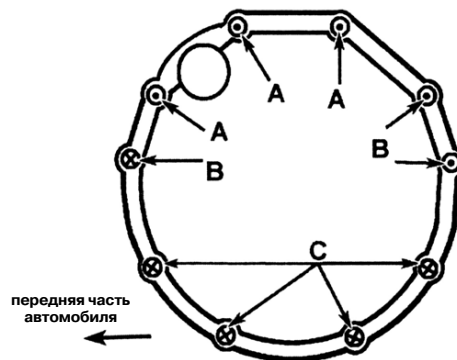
Монтажные болты коробки передач с ручным управлением (при установке см. буквы, которыми обозначены усилия затягивания резьбовых соединений, приведенные в спецификациях):
